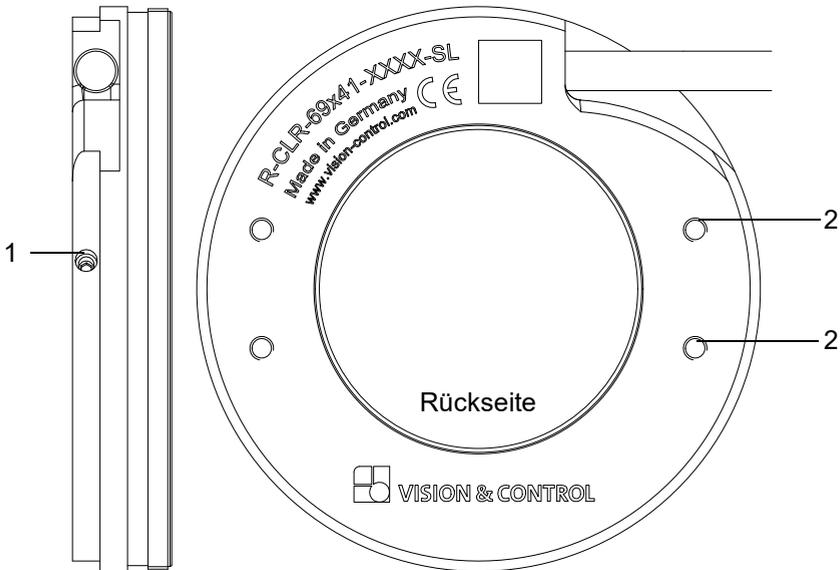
Position der Montagebohrungen und Gewindestifte
